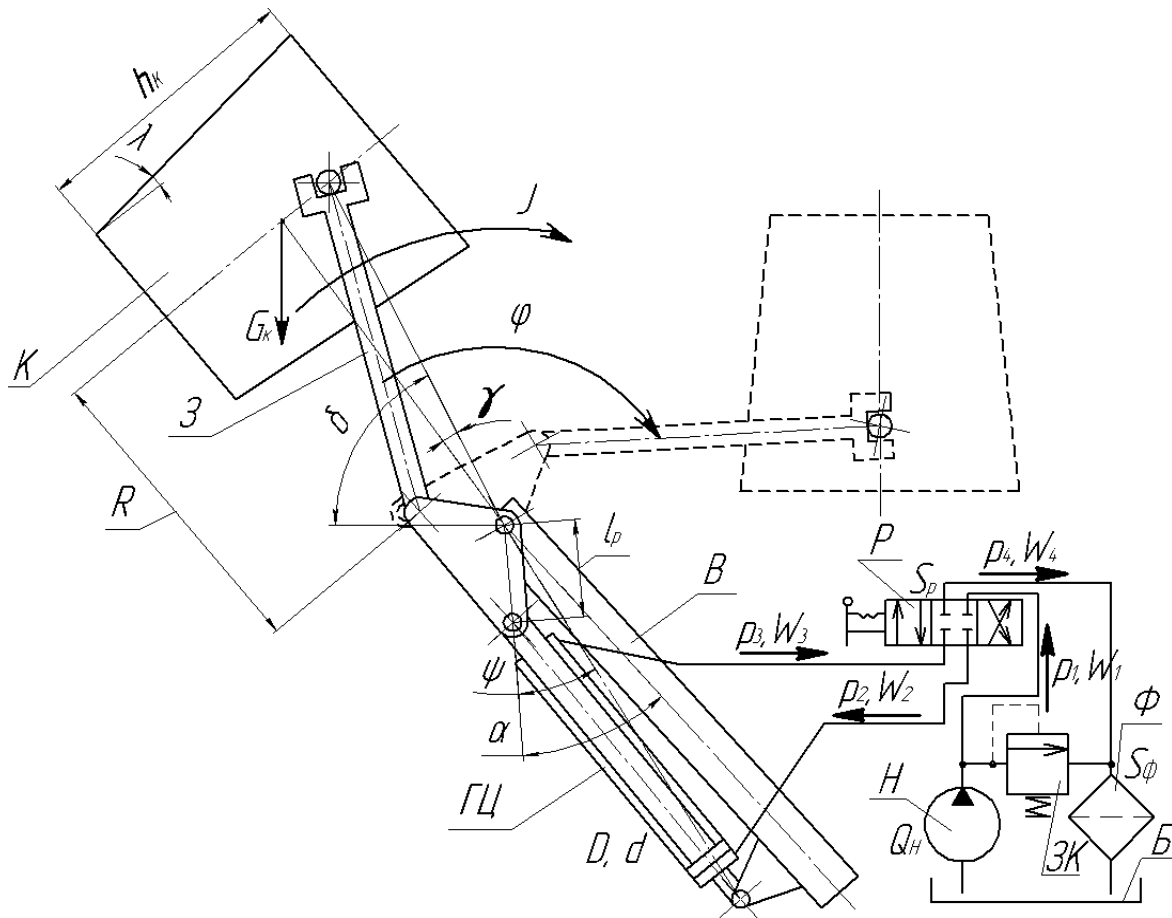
Розрахункова схема роботи гідроприводу перевертання контейнера
